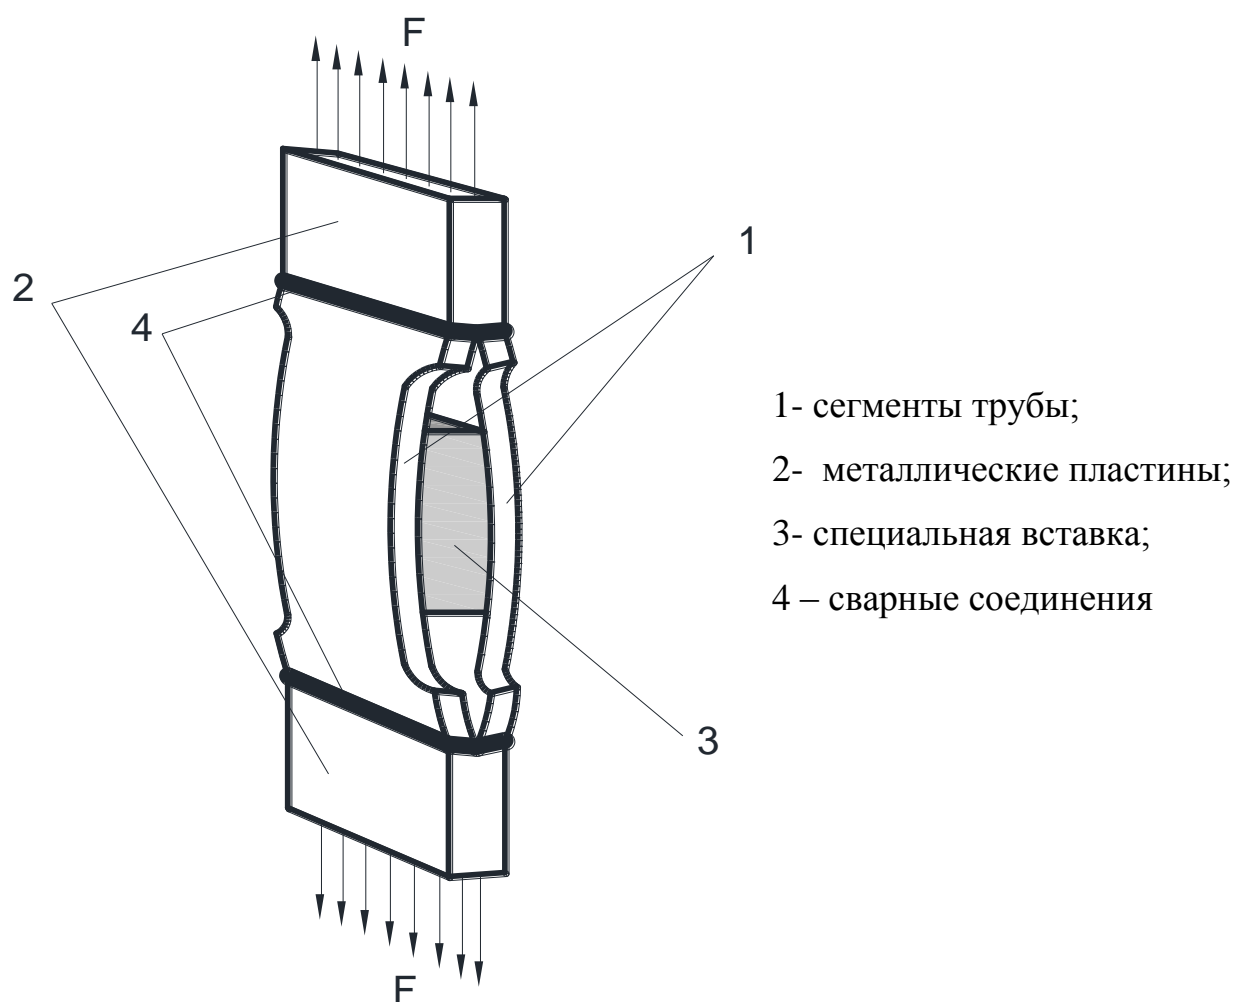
Конструкция образца для испытания металла труб при двухосном НДС
